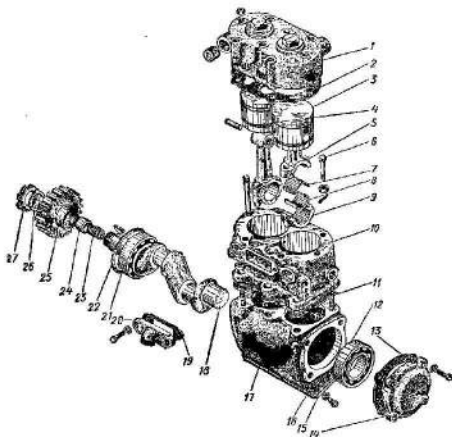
Компрессор пневматического тормоза: 1 – головка компрессора; 2 – прокладка головки; 3 – поршень; 4 – поршневой палец; 5 – шатун; 6 – шатуновый болт; 7 – верхний вкладыш; 8 – нижний вкладыш; 9 – крышка шатуна; 10 – блок цилиндров; 11 – прокладка блока цилиндров; 12 – подшипник; 13 – прокладка задней крышки; 14 – крышка картера задняя; 15 – крышка картера нижняя; 16 – прокладка нижней крышки компрессора; 17 – картер компрессора; 18 – вал коленчатый; 19 – прокладка впускного коллектора; 20 – впускной коллектор; 21 – подшипник; 22 – стопорное кольцо; 23 – пружина уплотнителя; 24 – уплотнитель; 25 – шестерня привода компрессора; 26 – шайба замочная; 27 – гайка.
